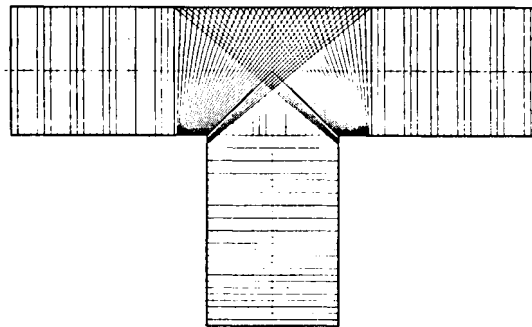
Намотка усиления в зоне соединения основной трубы и патрубка
